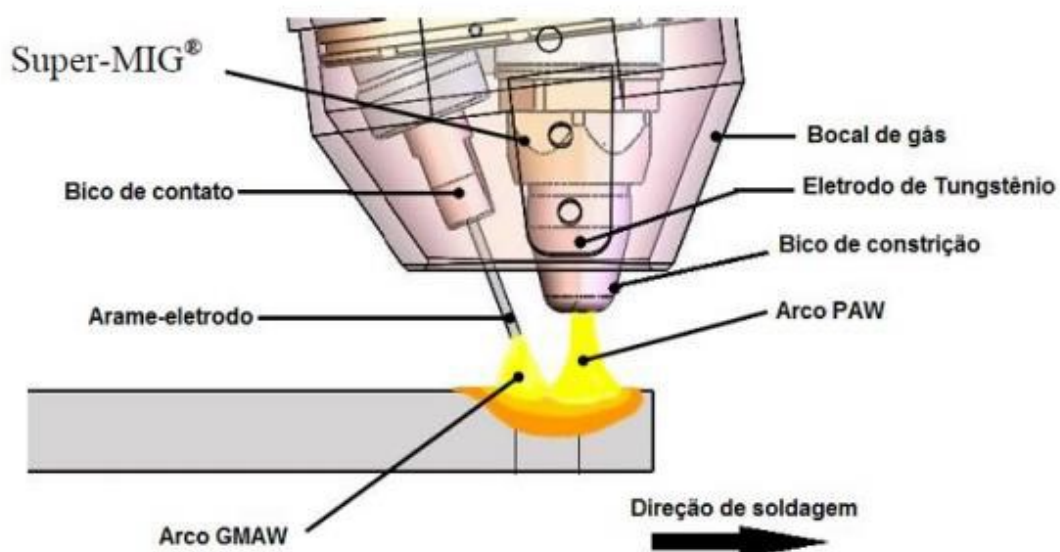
Esquema da tocha de soldagem no caso do processo Plasma-GMAW Serial (PLT, 2014).
